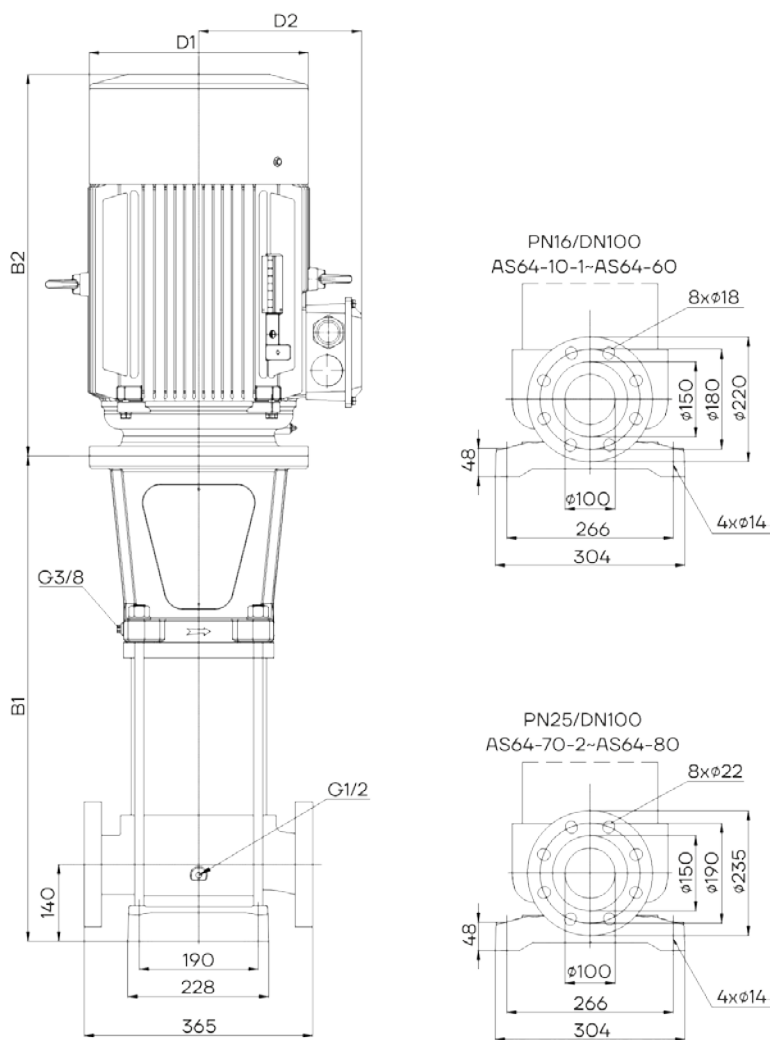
Ж Габаритно-присоединительные размеры VMB(F)-H 64
